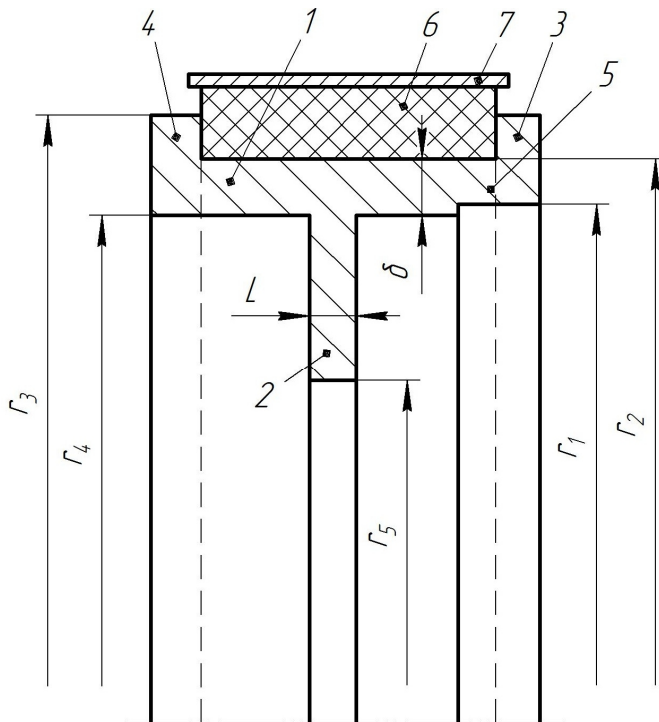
Конструктивные параметры тормозного шкива и его элементы: 1 – цилиндрическая оболочка; 2 – фланец; 3, 4 – реборды; 5 – цилиндрический диск; 6 – фрикционная накладка; 7 – тормозная лента
